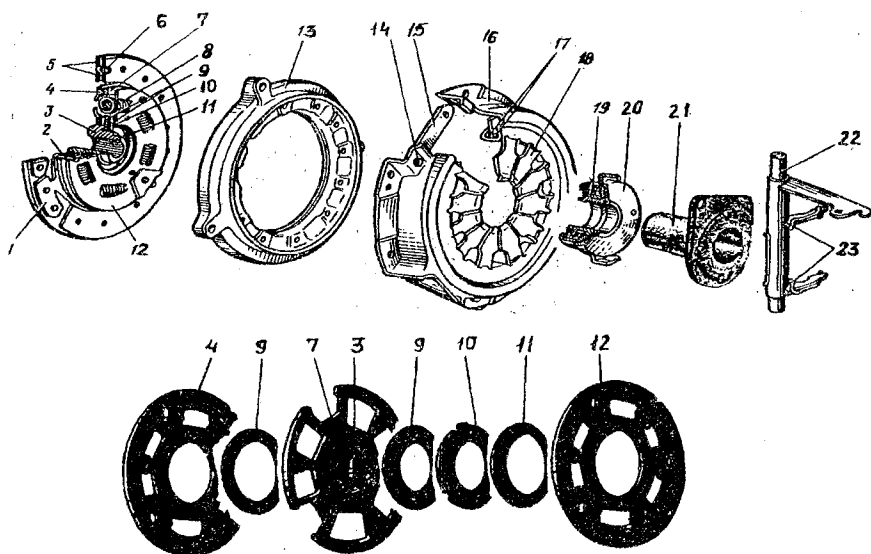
Детали однодискового сцепления и демпфера крутильных колебаний: 1 – ведомый диск сцепления; 2 – упорный палец; 3 – ступица ведомого диска; 4 – передняя пластина демпфера крутильных колебаний; 5 – фрикционные накладки; 6 – заклепка для крепления фрикционной накладки; 7 – фланец ступицы ведомого диска; 8 – пружина демпфера; 9 – фрикционные кольца демпфера; 10 – опорное кольцо пружинной шайбы демпфера; 11 – пружинная шайба демпфера; 12 – задняя пластина демпфера крутильных колебаний; 13 – нажимной диск сцепления; 14 – заклепка для крепления упругих пластин; 15 – упругая пластина; 16 – кожух сцепления; 17 – опорные кольца нажимной тарельчатой пружины; 18 – нажимная тарельчатая пружина; 19 – подшипник выключения сцепления; 20 – муфта подшипника выключения сцепления; 21 – направляющая втулка; 22 – вилка выключения сцепления; 23 – соединительная пружина вилки и муфты подшипника выключения сцепления
